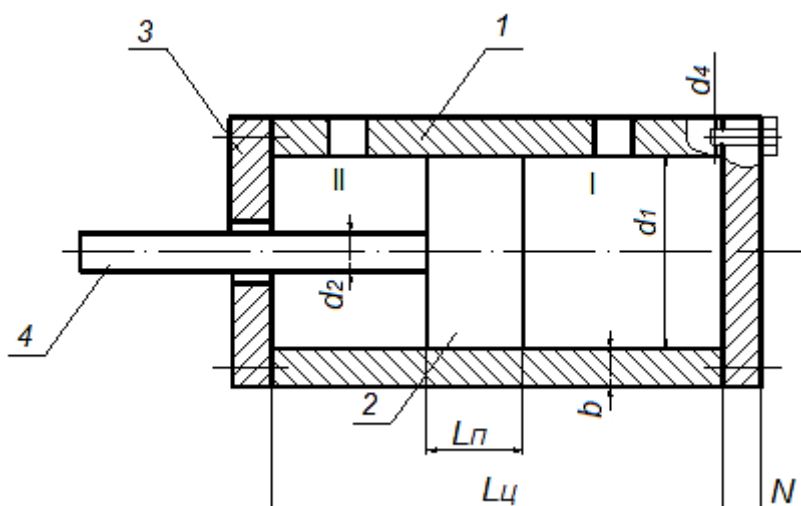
Конструктивные размеры гидроцилиндра подводящего устройства:
